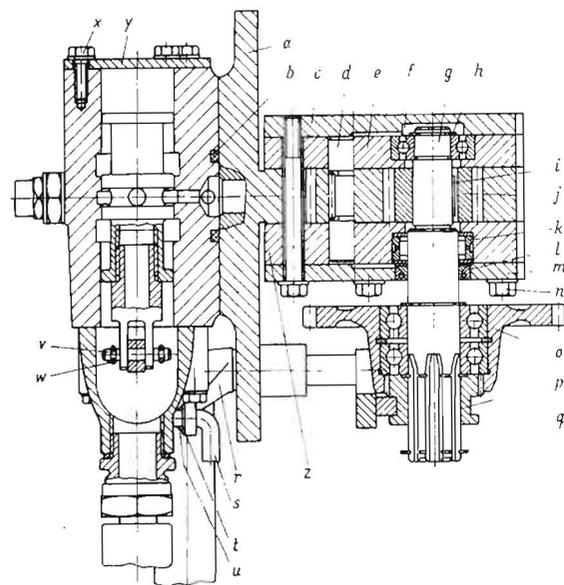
Hydraulikpumpe mit Steuerschieber. a Mittelplatte, b Dichttring, c Lagerdeckel, links, d Achse, e Lagerflansch, links, f Wälzlager, g Antriebswelle, h Soegerring, i Keil, j Zahnrad, k Nadellager, l Radialdichttring, m Lagerdeckel, rechts, n Ankerschraube, o Antriebsrad, p Schalthülse, q Soegerring, r Schalthobel, s Schaltstange, t Scheibe, u Splint, v Rundring, w Bolzen, x Sechskantschraube, y Deckel, z Lagerflansch, rechts
